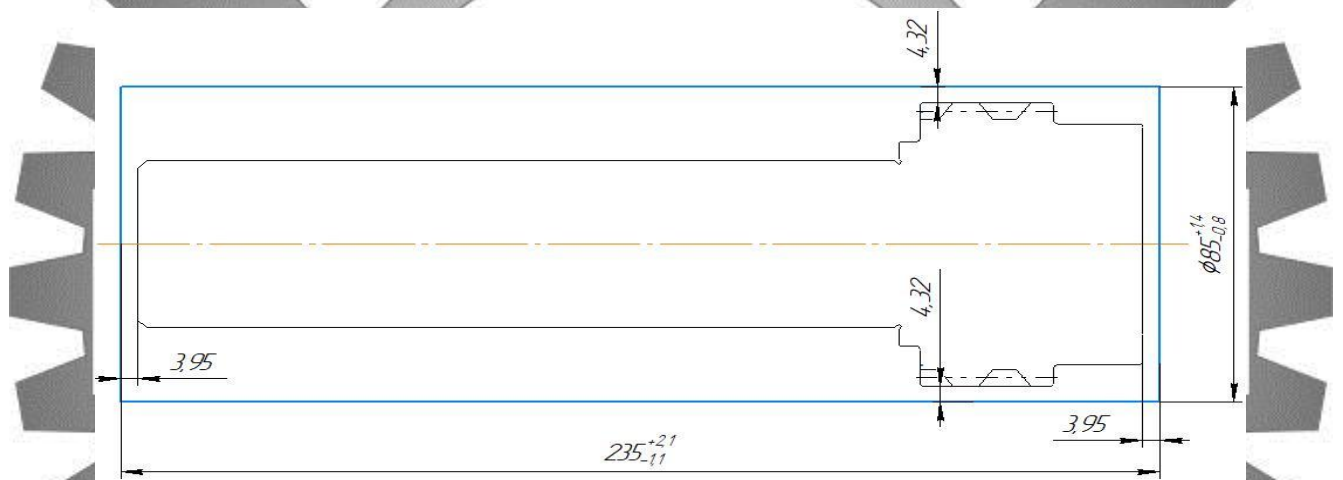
Заготовка, яка виготовлена із круглого прокату
